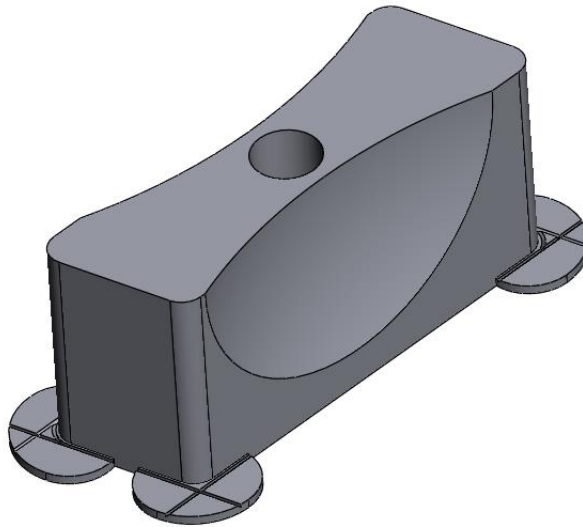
Imagen del CAD de la pieza 2 con los soportes lista para comenzar el proceso de impresión.
